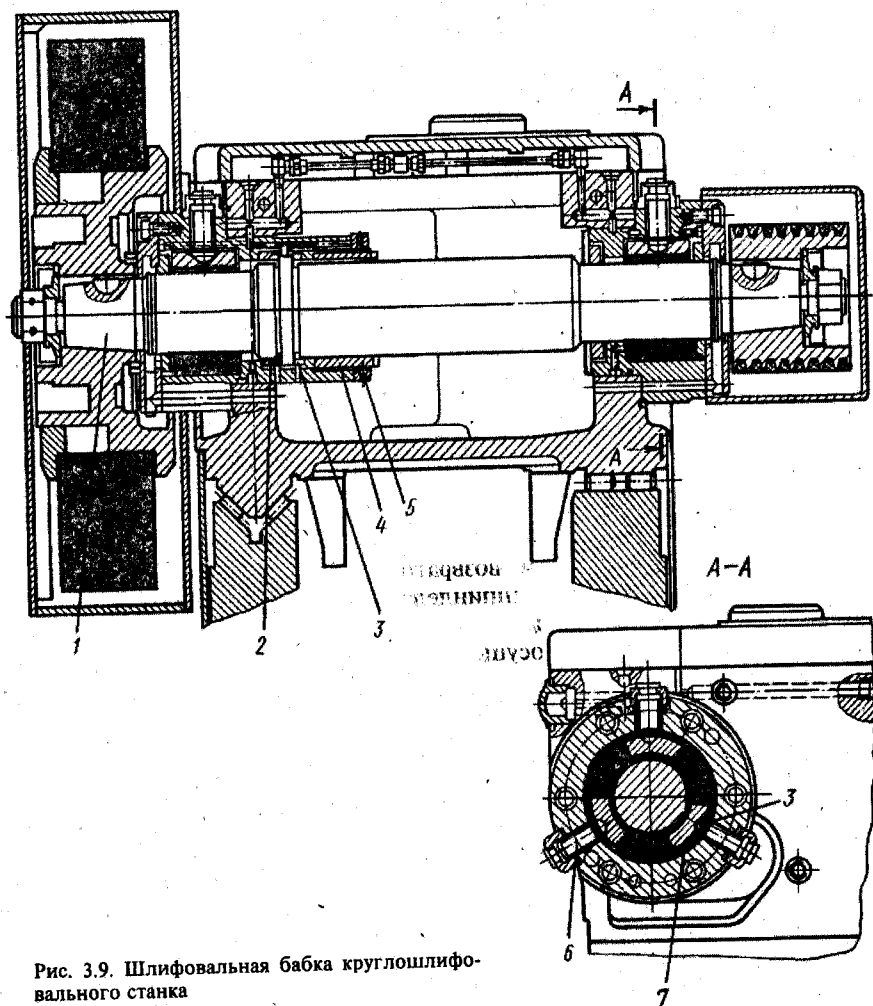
Шлифовальная бабка круглошлифовального станка
